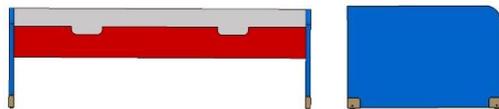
ALZADO Y PERFIL CAMA NIDO
